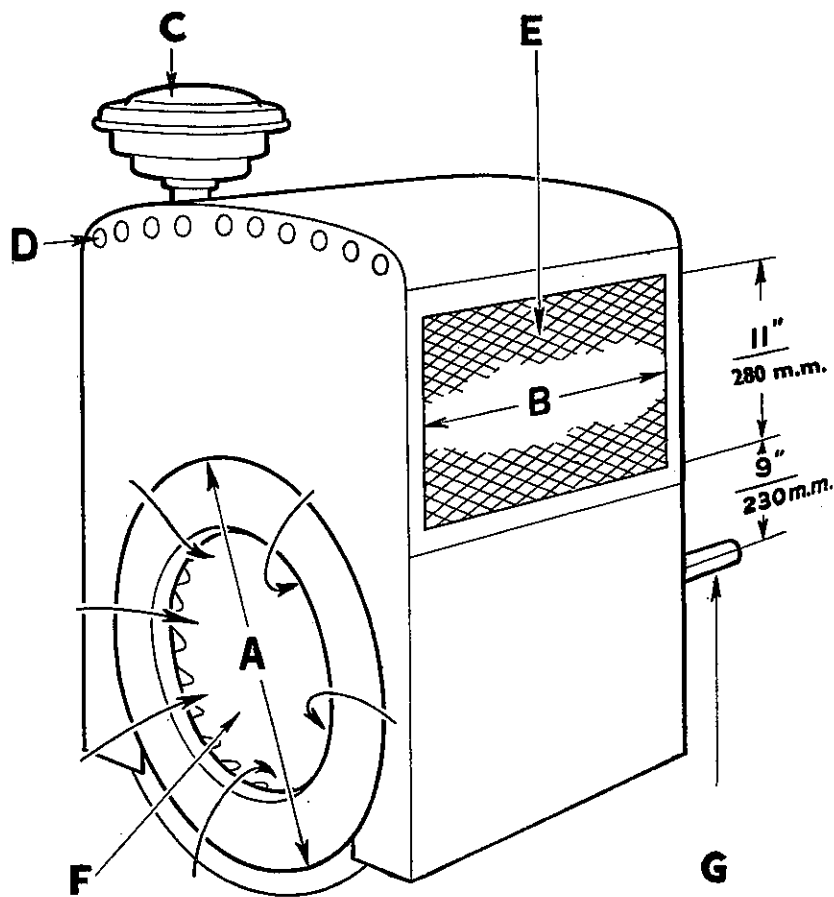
Motor in omkasting, het geheel opgesteld in de buitenlucht
